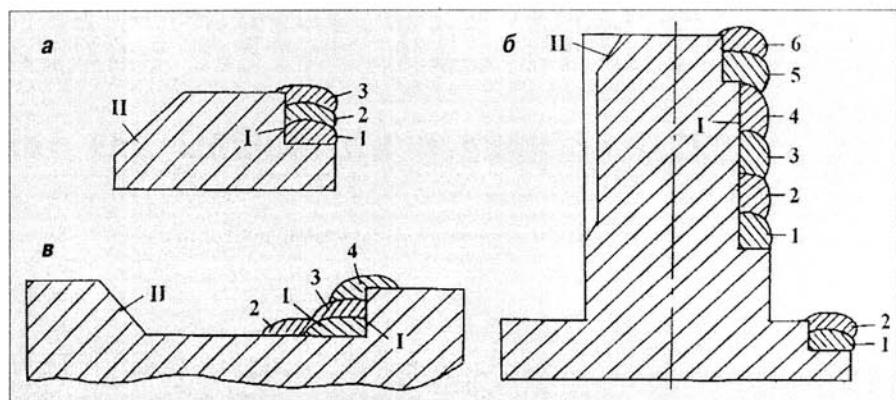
Подготовка (обозначена цифрами) кромок для наплавки штампов: I – правильно; II – неправильно; а – режущие кромки; б – поверхность пресс-штампа; в – поверхность паза или ручья
